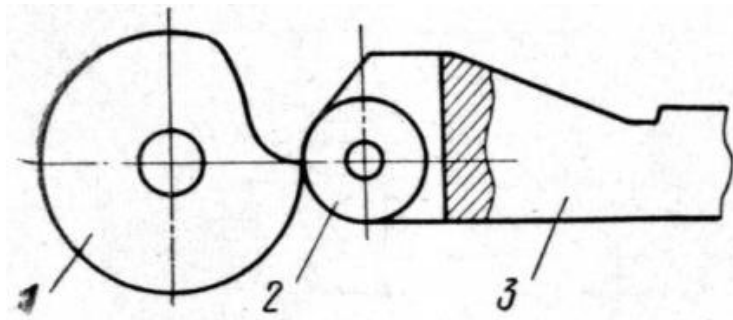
Эскиз установки ролика рейки суппорта на кривой кулачка: 1 – кулачек; 2 – ролик; 3 – рейка суппорта.
